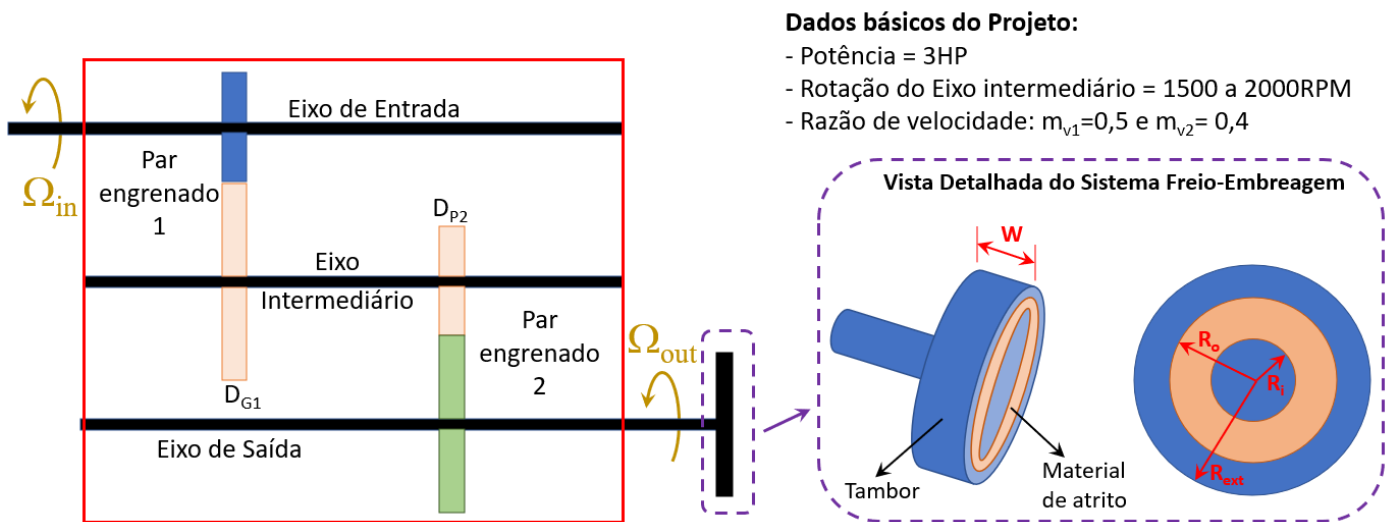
Trem de engrenagem composto – Redutor de Velocidades.
